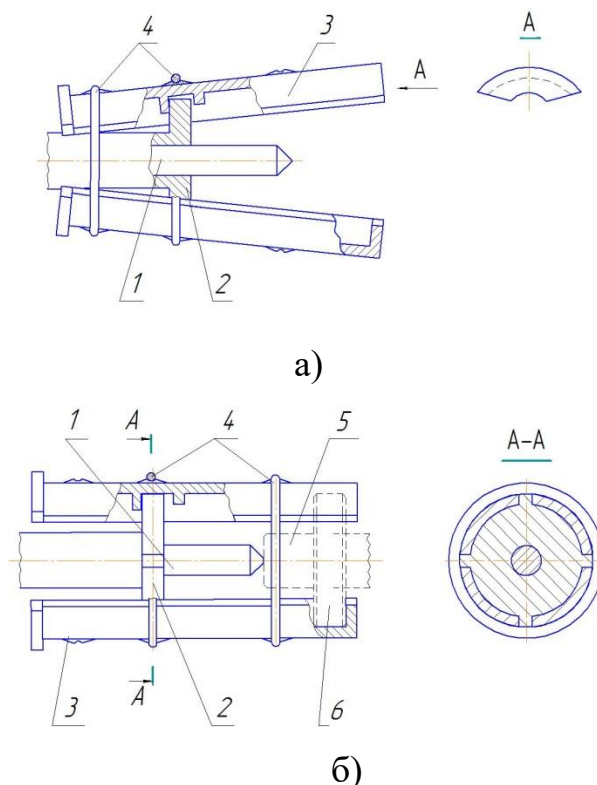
Знімач підшипників з коливними лапами циліндричної форми: а) положення розведеного стану; б) положення захопленого стану; 1 – шток гідроциліндра; 2 – опора; 3 – лапа; 4 - еластичні стяжні кільця; 5 – вал; 6 – підшипник.
